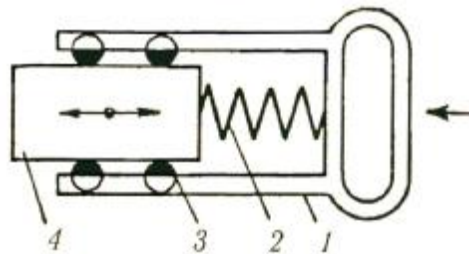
Схема віброізолюваного держака: 1 – держак; 2 – пружний елемент; 3 – підшипник; 4 - корпус
